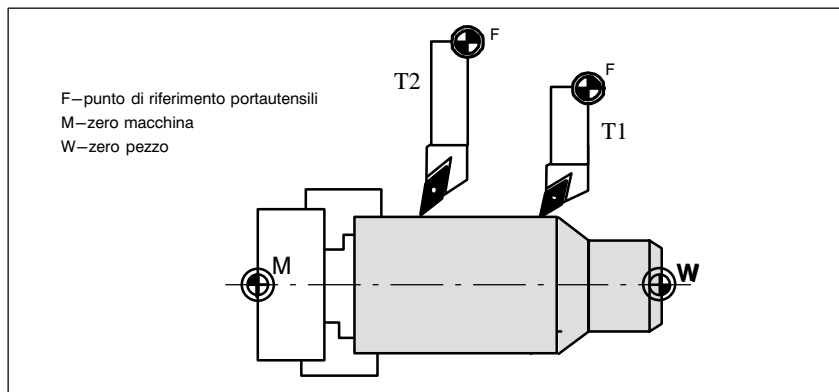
Lavorazione di un pezzo con utensili di dimensioni diverse
